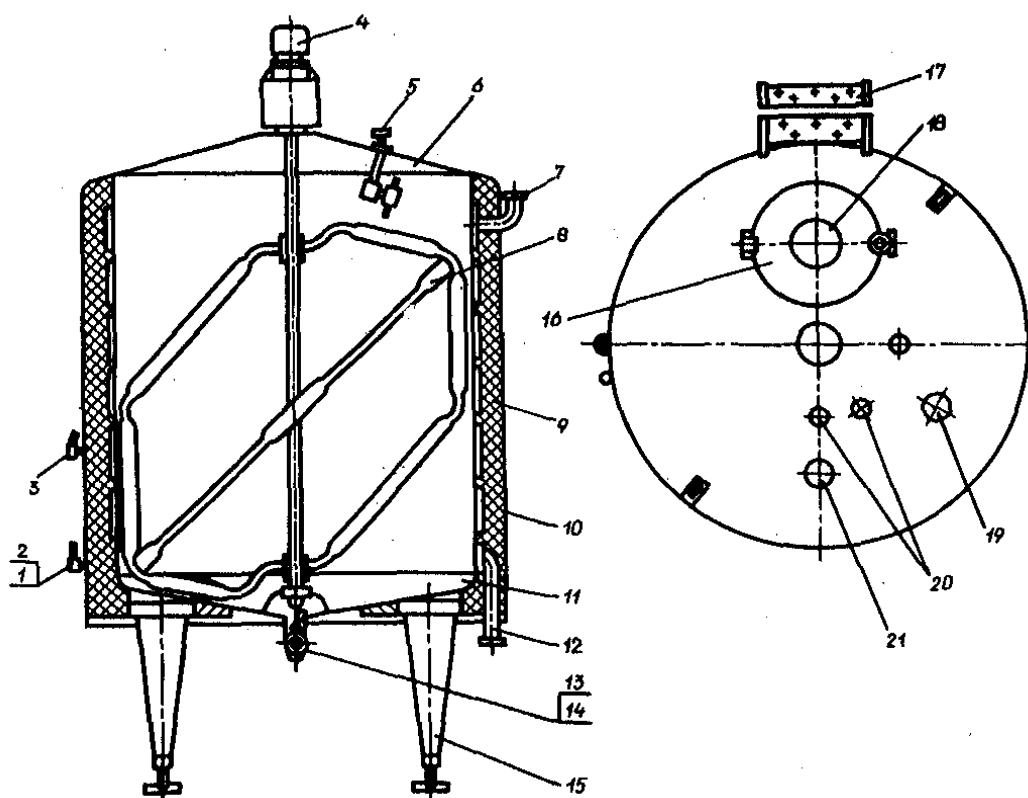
Общий вид резервуара Я1–ОСВ в разрезе
